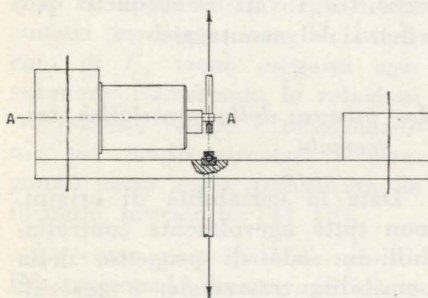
Dispositivo di taratura di un dinamometro a due componenti.
